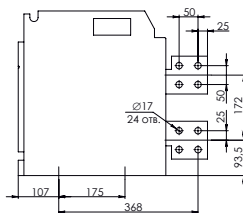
Габаритные размеры выдвижных четырехполюсных выключателей типоразмера E In = 1600, 2000 А
